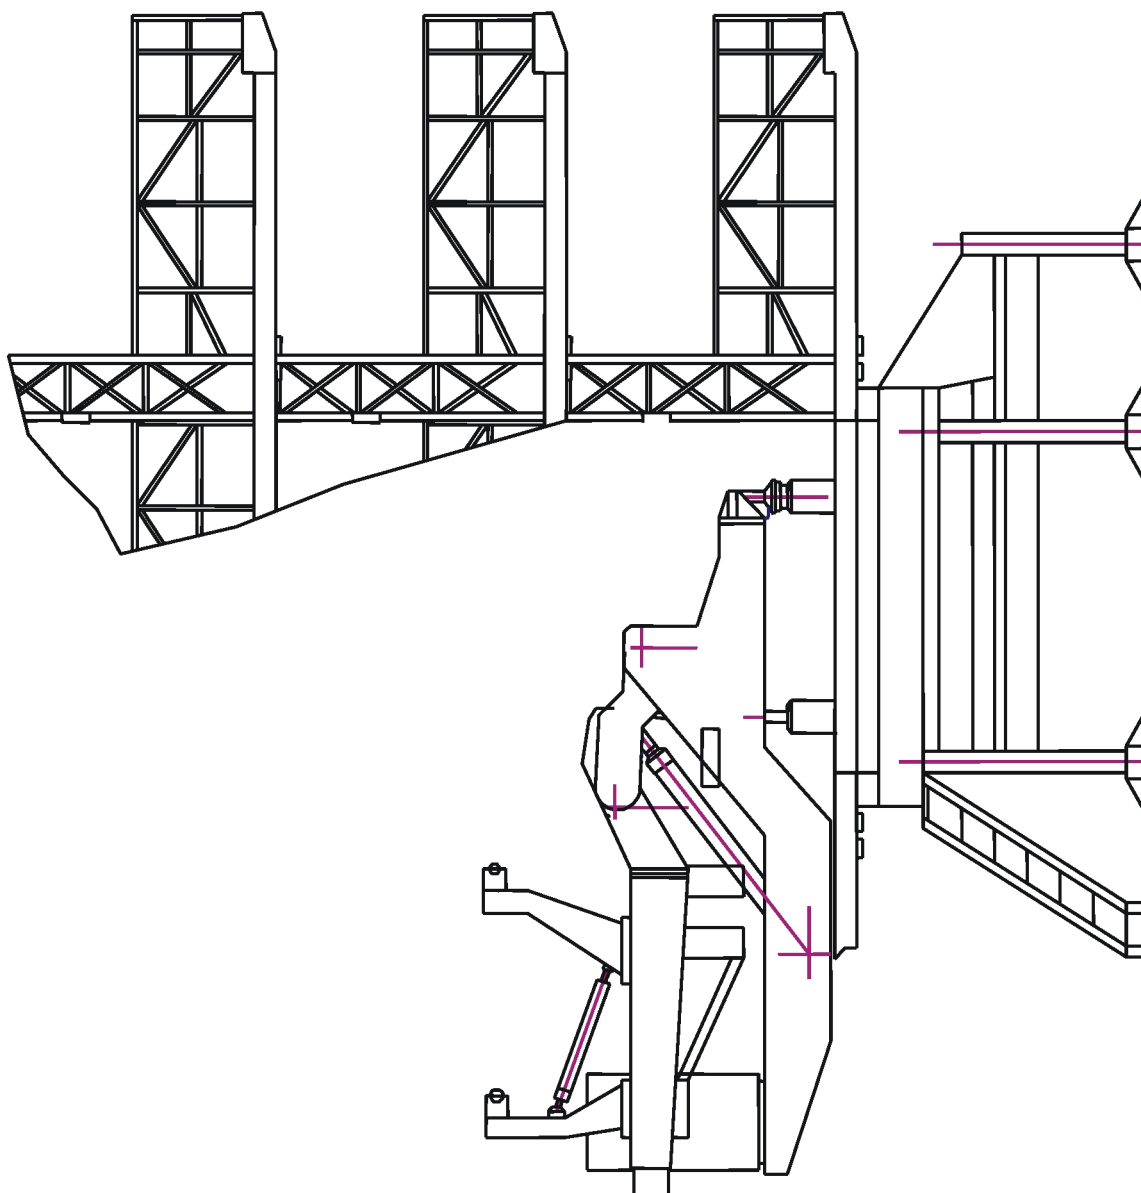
Схема размещения агрегата наклона 17Т17 на стенде 11Т326
